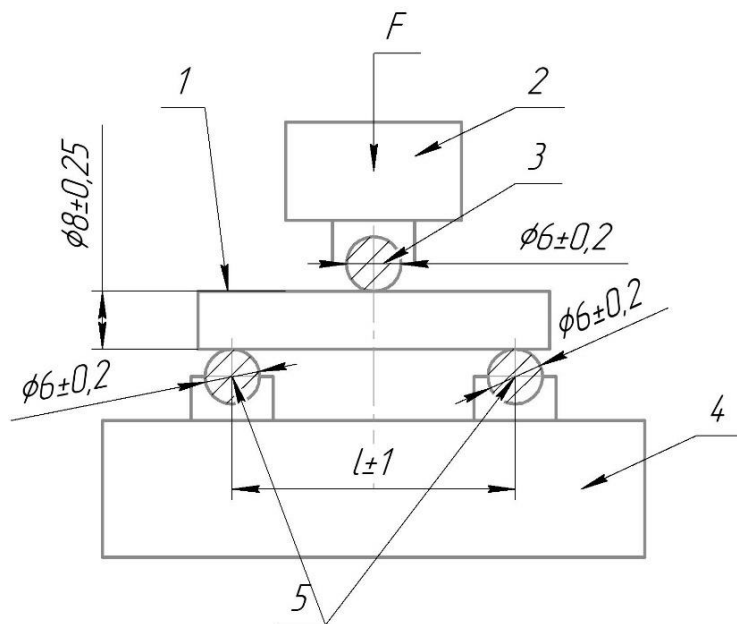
Схема стенда: 1 – зразок твердого сплаву; 2 – рухливий поршень; 3 – циліндрична навантажувальна опора; 4 – нижня плита преса; 5 – циліндричні нерухомі опори, що вільно лежать
